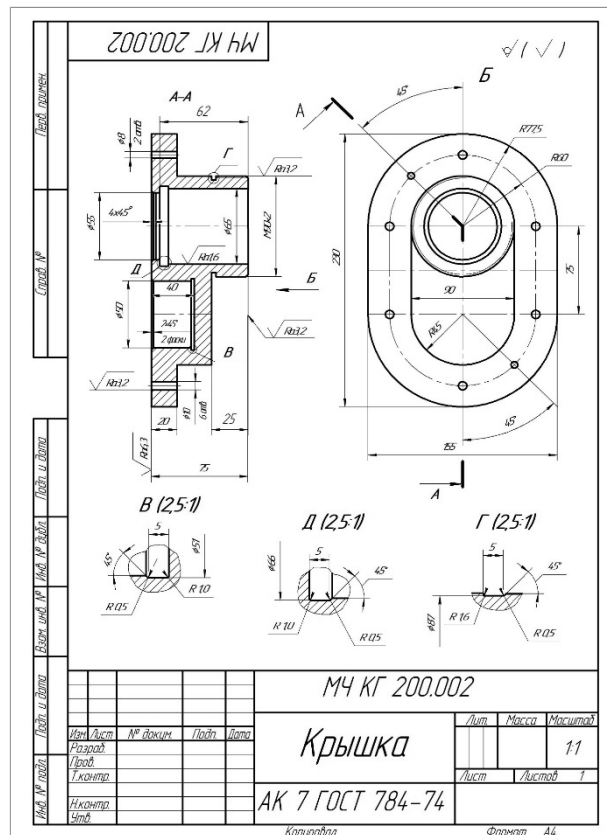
Рабочий чертёж «Крышка», позиция 2
